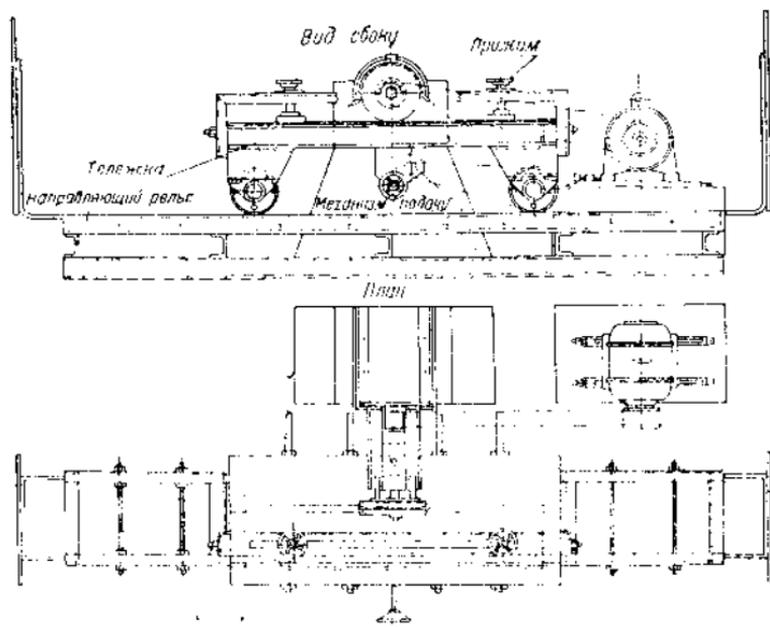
Фрезерный станок с ручной подачей (вид сбоку и сверху)
